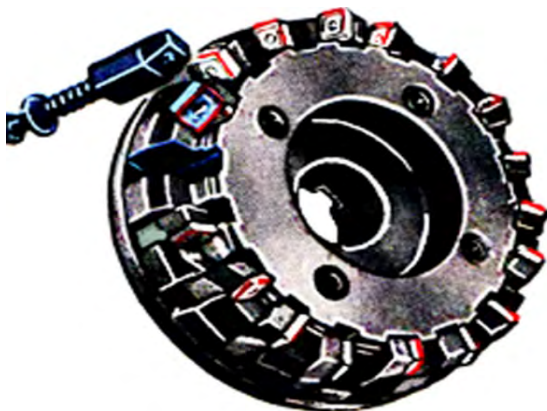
Торцовая фреза с механическим креплением твердосплавных пластин
